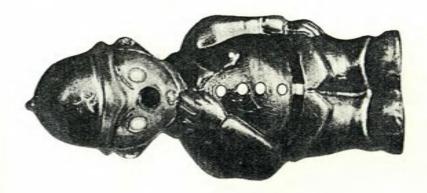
Gespritzte Cerrocastmaske zum Farbenspritzen,
